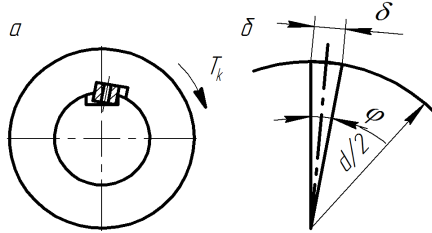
Схема деформації пружної призматичної шпонки у з'єднанні: а – положення маточини відносно вала; б – зв'язок δ з d через кут φ
